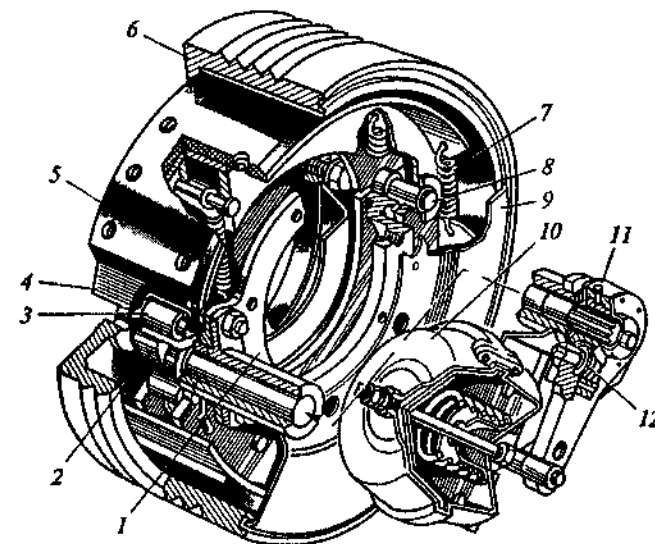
Колесный тормозной механизм грузового автомобиля МАЗ: / — суппорт; 2 — кулак; 3 — ролик; 4 — колодка; 5 — накладка; 6 — тормозной барабан; 7 — пружина; 8 — ось; 9 — щиток; 10 — тормозная камера; 11 — рычаг; 12 — червячный механизм
